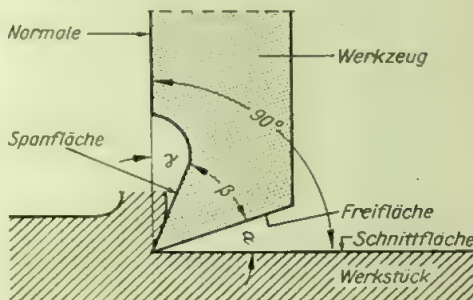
Winkel und Flächen an der Schneide
